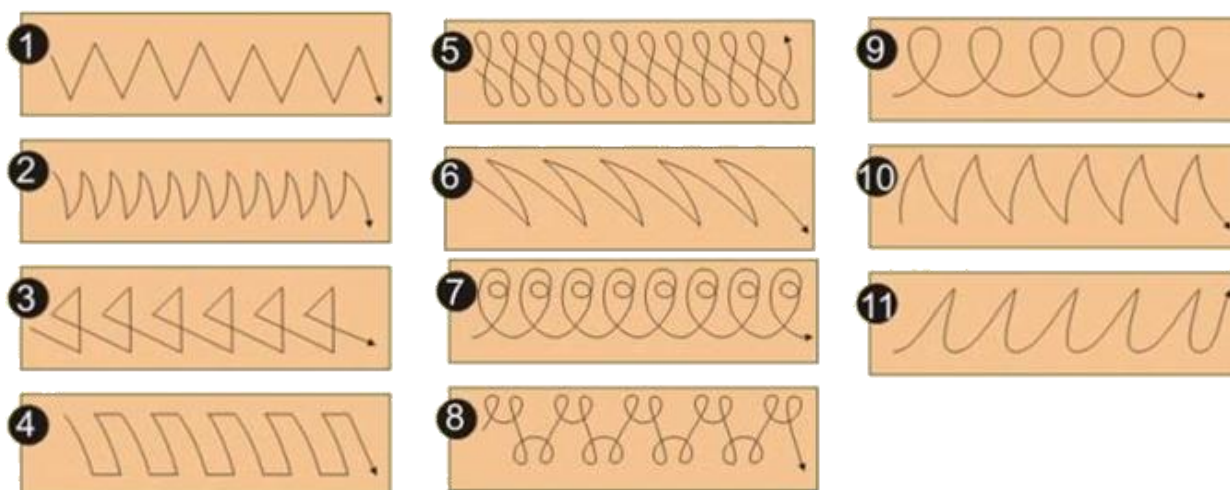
Рекомендуемые траектории перемещения сварочного электрода во время сварки
